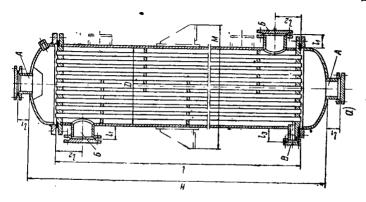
Одноходовой теплообменный аппарат типа ТН с диаметром корпуса 159 или 273 мм, имеющий две камерные сварные крышки с плоскими донышками.
